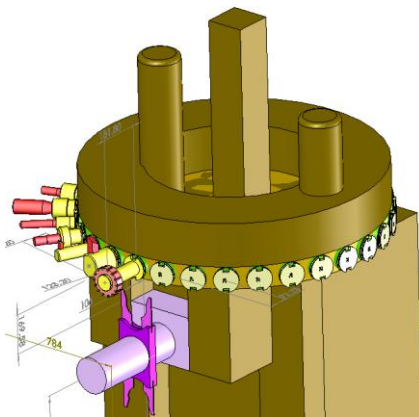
Інструментальний магазин багатоцільового верстата MAST\_MM855\_S24
